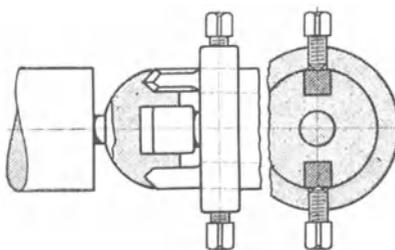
Einschuppen der Ringnut mit Bohrstange.
